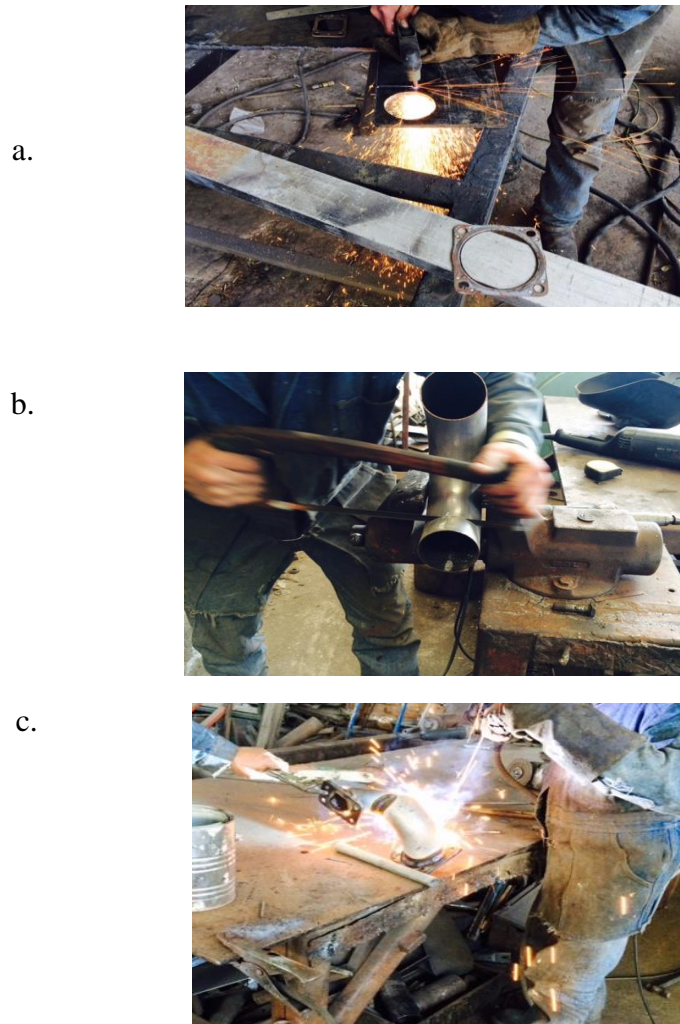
(a) Proceso de corte de las bases, (b) Proceso de doblaje y corte del tubo galvanizado, (c) Proceso de soldadura de la pieza conjunta para los gases de escape
